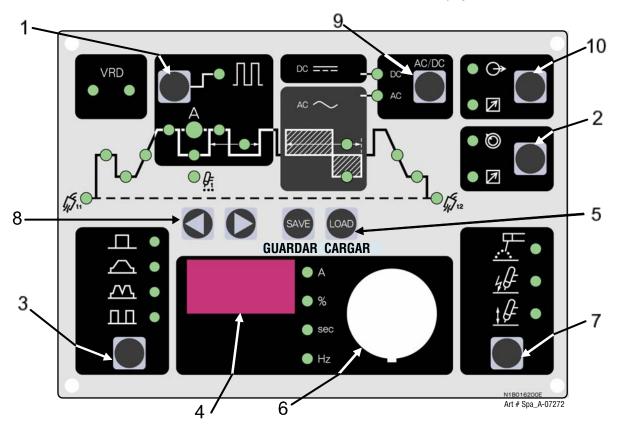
Panel delantero de la máquina 300 AC/DC
